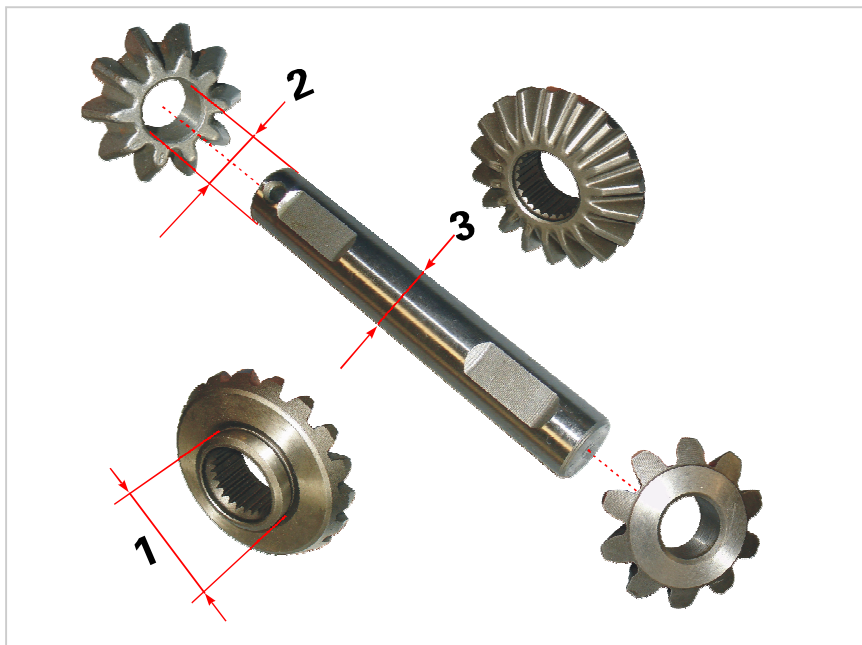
半轴齿轮、行星齿轮和行星齿轮轴的检查部位
